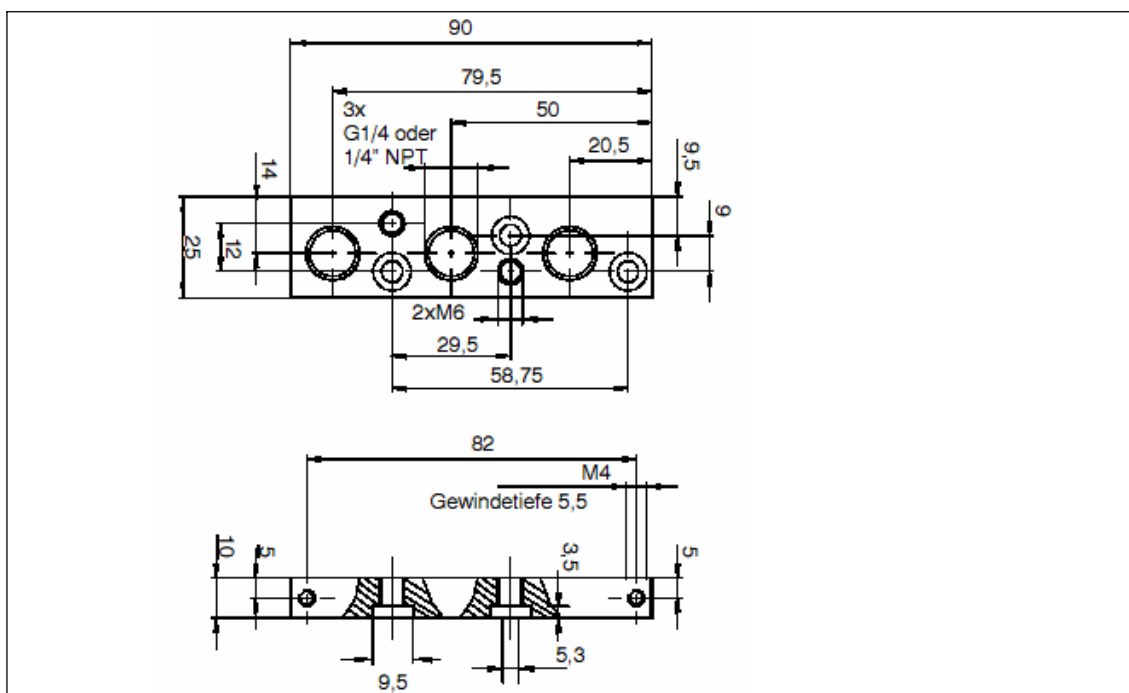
Габаритный чертеж соединительной планки для пластикового корпуса
